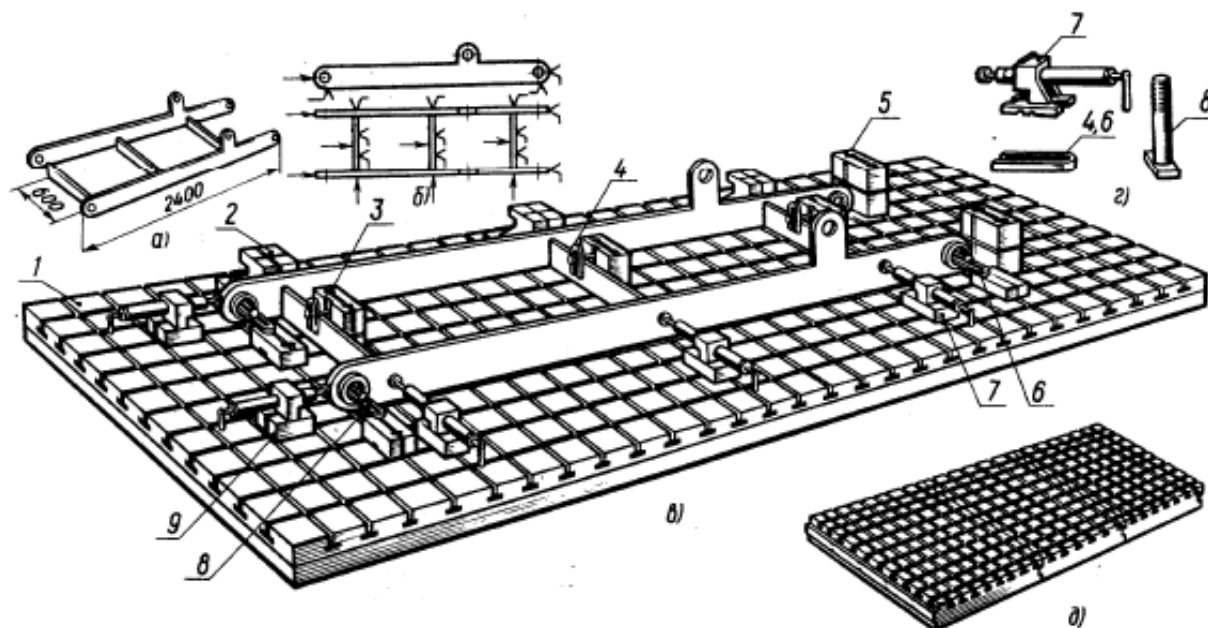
Компоновка СРПС: *а*) изделие; *б*) схема базирования; *в*) приспособление с изделием; *г*) детали СРПС; *д*, 1) опорная плита; 2) базовые неподвижные элементы; 3) болт, 4) прихват; 5, 9) корпусные детали; 4, 6) прижим; 7) подвижный упор; 8) болт крепежный.
